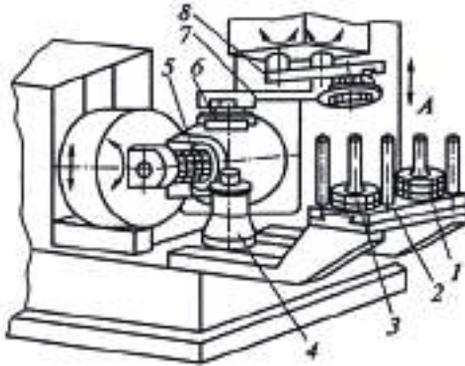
Типовое загрузочное устройство, встроенное в зубофрезерный станок: 1 – заготовка; 2 – кассета; 3 – обработанная деталь; 4 – зажимное устройство; 5 – фреза; 6 – захват; 7, 8 – поворотные руки
